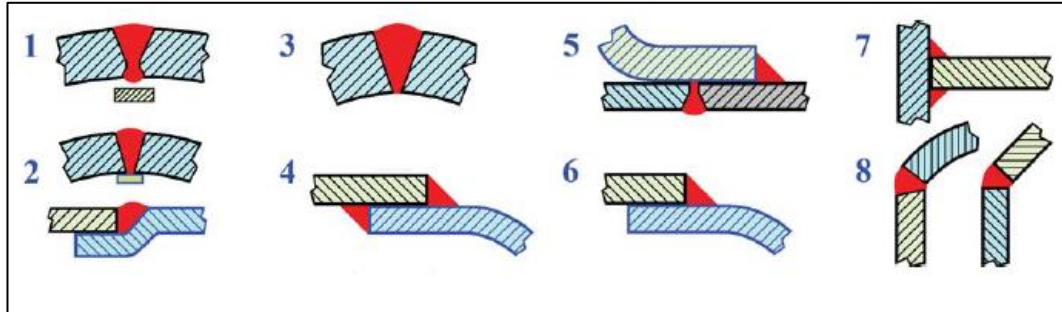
Tipos de soldaduras permitidas.
